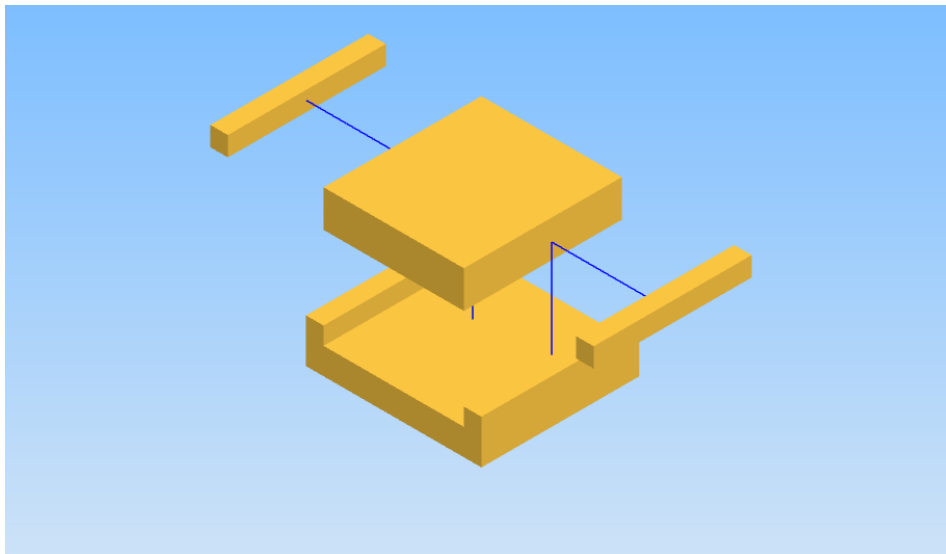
Vista explosionada de la pieza mostrada en la figura 3.44. Esta pieza se construyó en partes para hacer una animación donde solo se modifiquen las escalas de cada componente.
